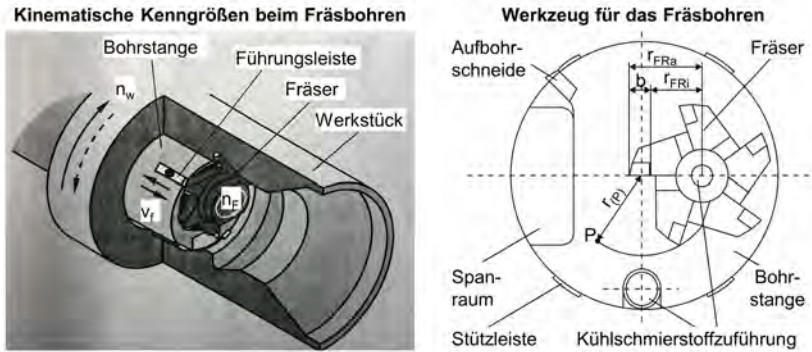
Fräsbohren: Kinematik und Werkzeug [Tuf87, Utz90]
